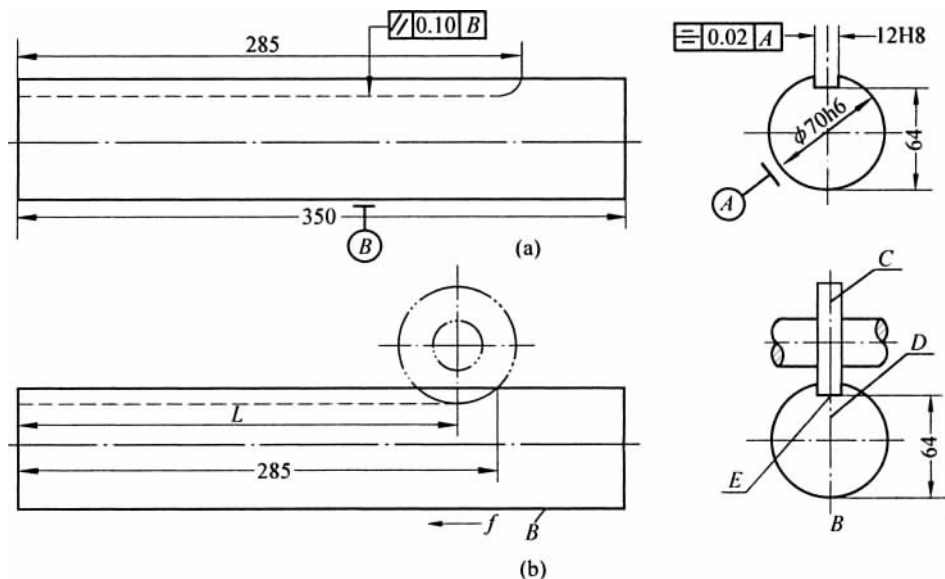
尾座套筒工件铣键槽工序及工件加工时的正确位置
